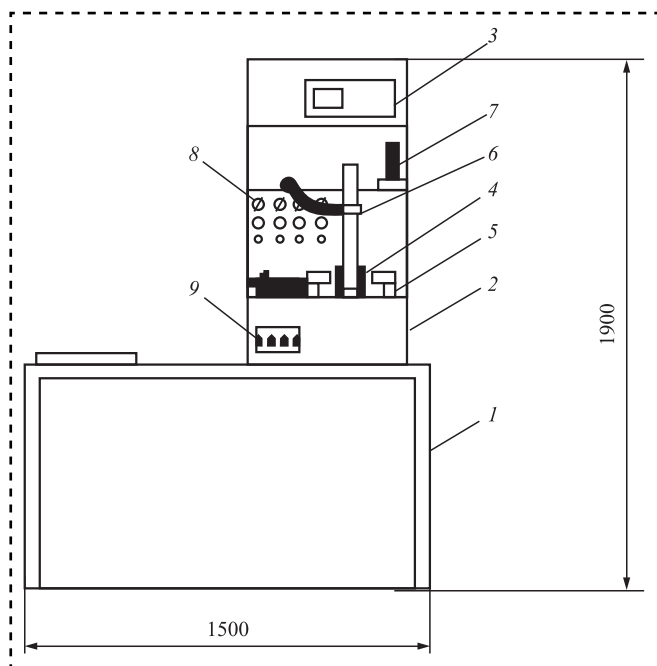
Принципиальная схема станка полуавтоматической заштамповки:
